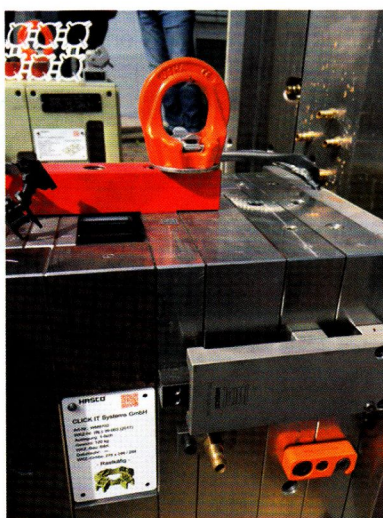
Spritzgießwerkzeug mit Klinkenzug, Ringschraube, Werkzeugsicherung und Typenschild
